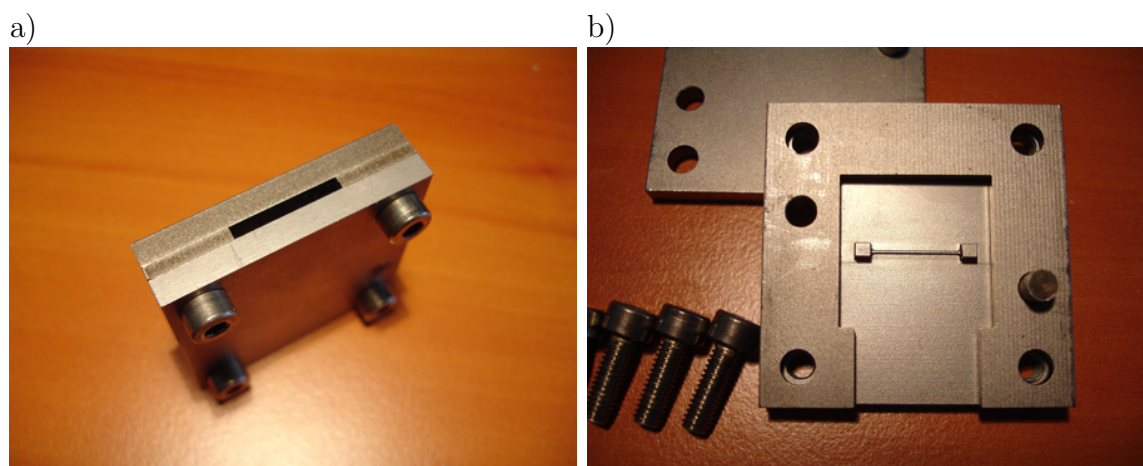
Moule micrométrique assemblé avec l'ouverture de remplissage en haut (a). Moule micrométrique contenant le canal micrométrique intégré de section carrée $300\mu m$ (b).
